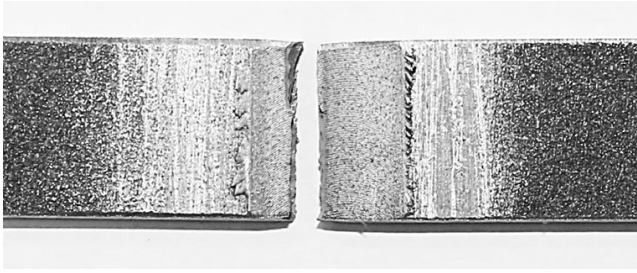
Разрушение сварных образцов соединений, полученных сваркой трением с перемешиванием, при испытании на статическое растяжение
